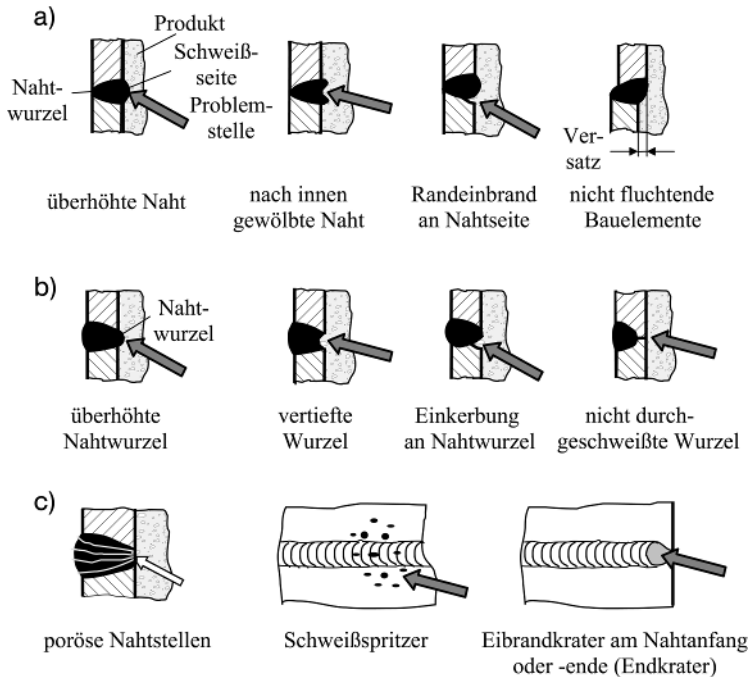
Darstellung von Schweißnahtfehlern:
